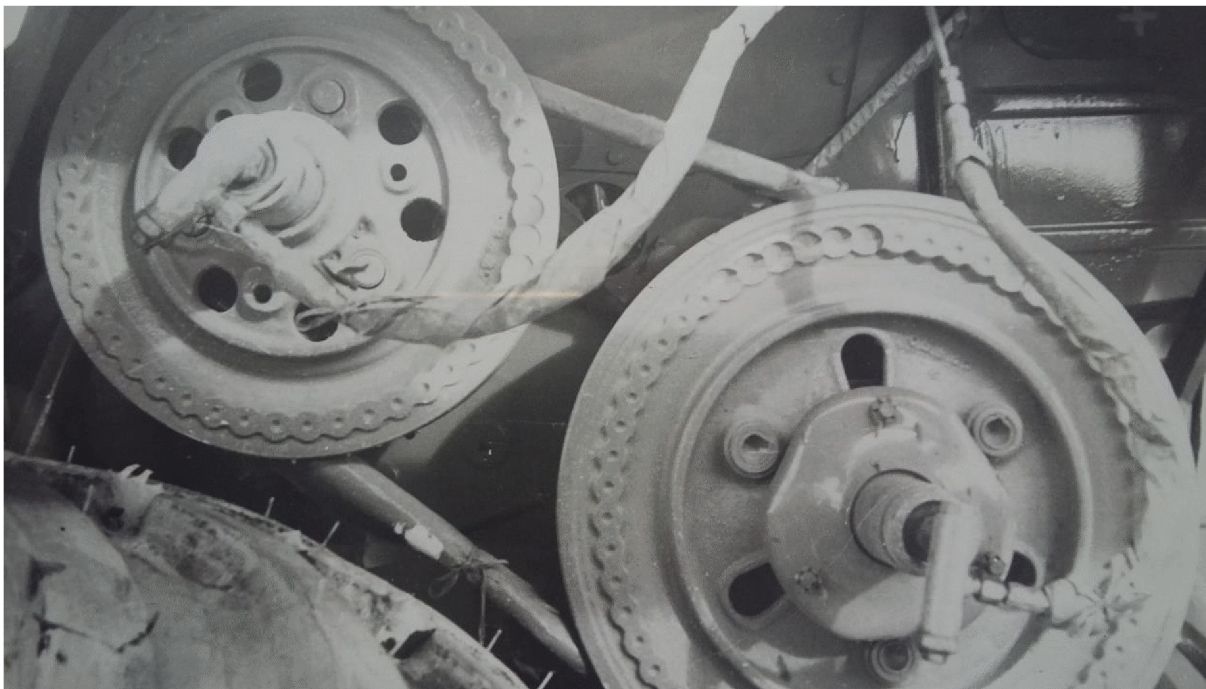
Загальний вид варіаторного привода молотильного барабана зернозбирального комбайна
